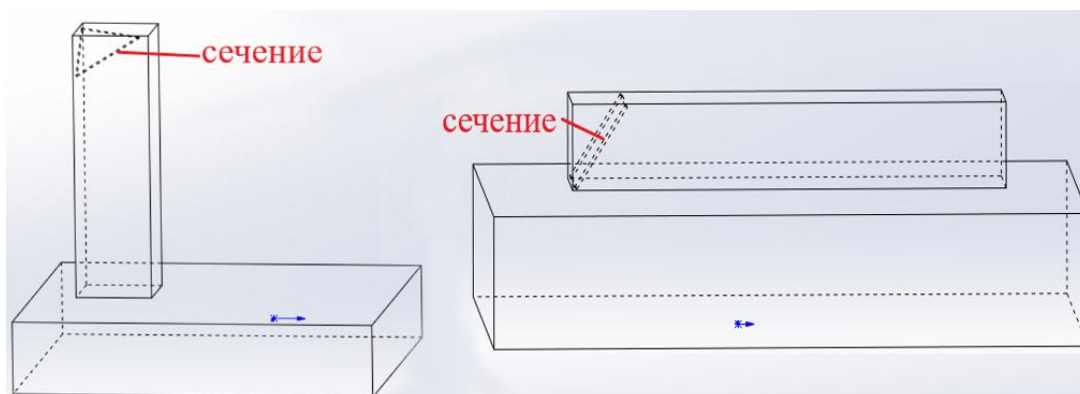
Вертикальная заготовка и горизонтальная заготовка
